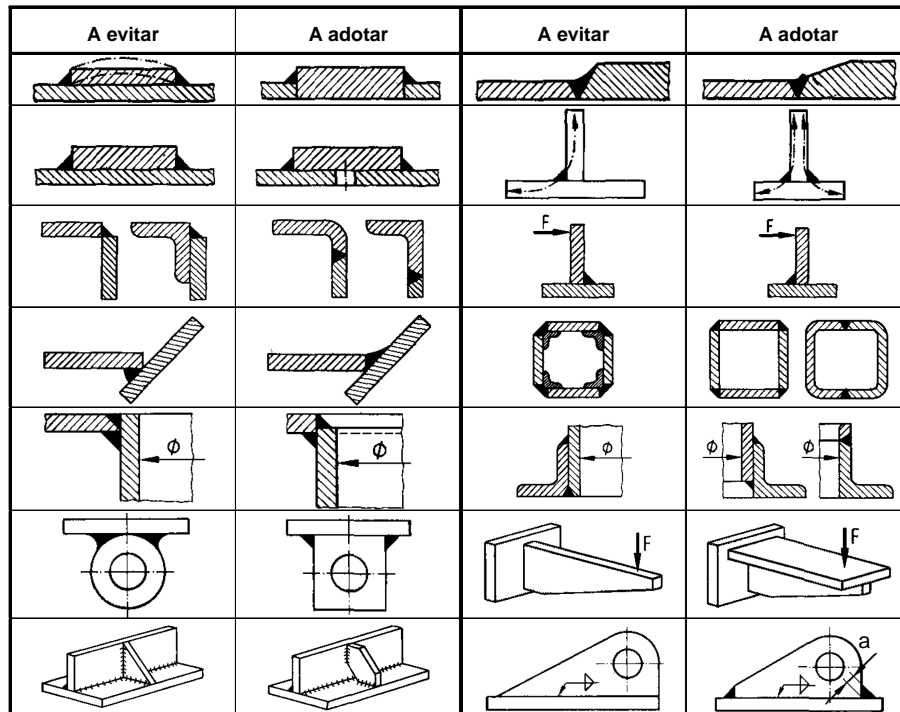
Exemplos de concepções de juntas soldadas. Adaptada de [F1]
